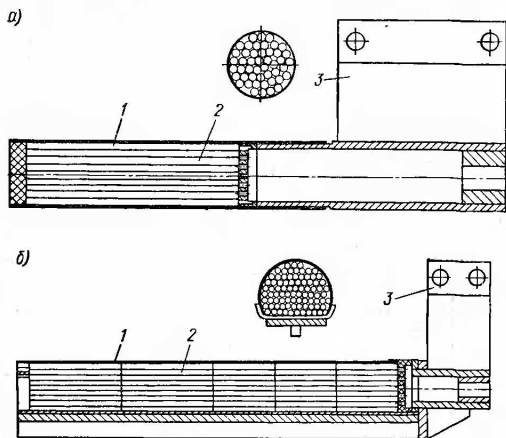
Ферритовые сердечники: а — цилиндрического сечения; б — сегментного сечения; 1 — ферритовые стержни; 2 — защитный кожух; 3 — плиты крепления
